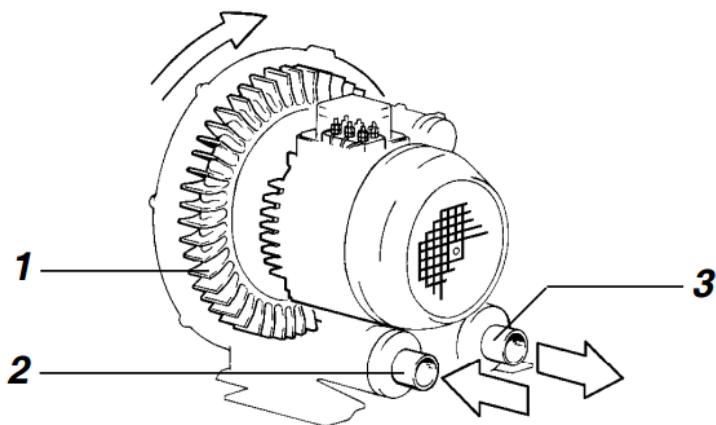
Устройство одноступенчатой вихревой воздуходувки RB
